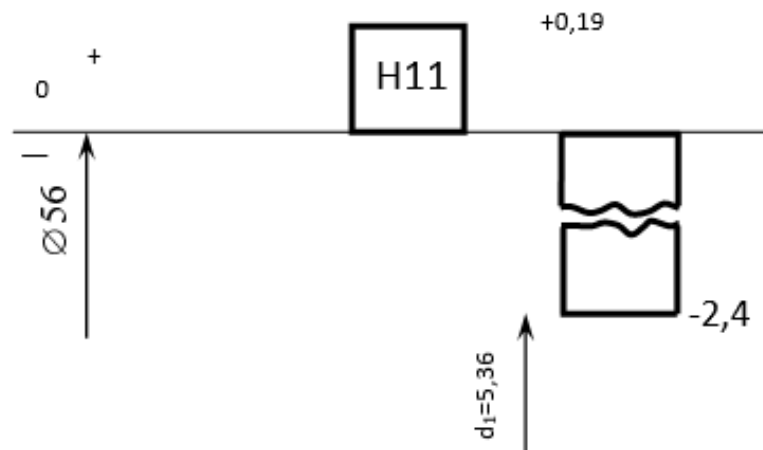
Схема розташування полів допусків шліцьового з'єднання 8x56x62 за розміром d при центруванні за D або b
